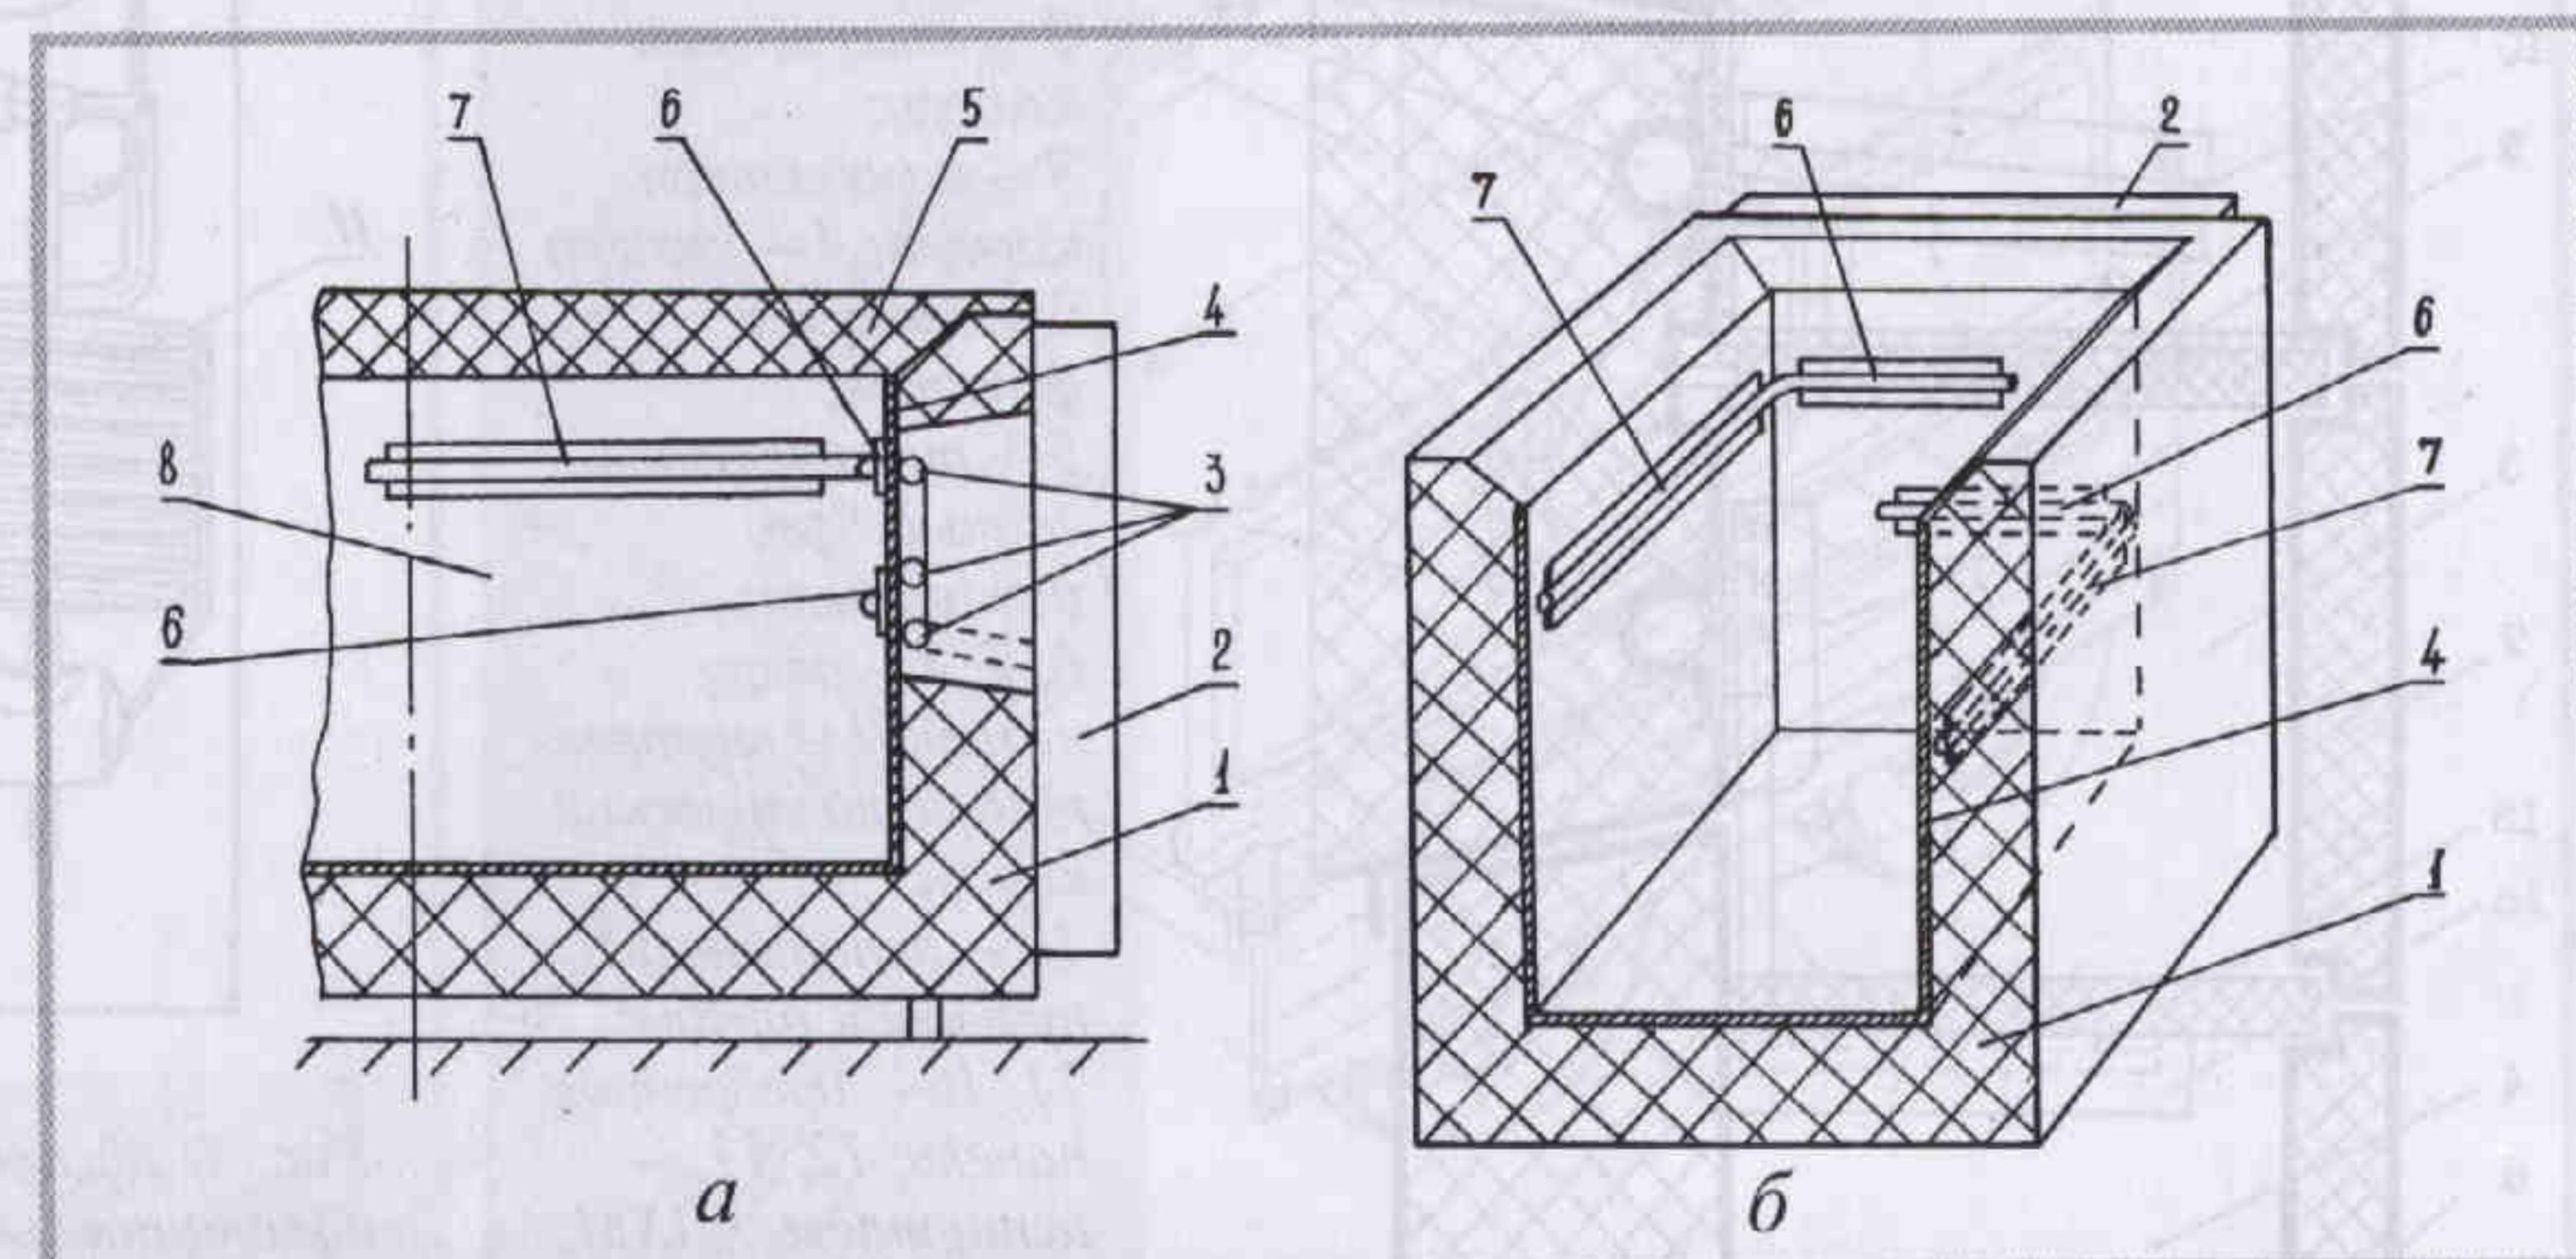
Абсорбционный холодильный аппарат типа «ларь» с тепловыми трубами: а – разрез (вид сбоку); б – общий вид; 1 – корпус (теплоизолированный блок); 2 – АДХМ; 3 – испаритель АДХМ; 4 – внутренний металлический корпус; 5 – крышка ларя; 6 (7) – конденсатор (испаритель) тепловой трубы; 8 – полезный объем холодильной камеры
